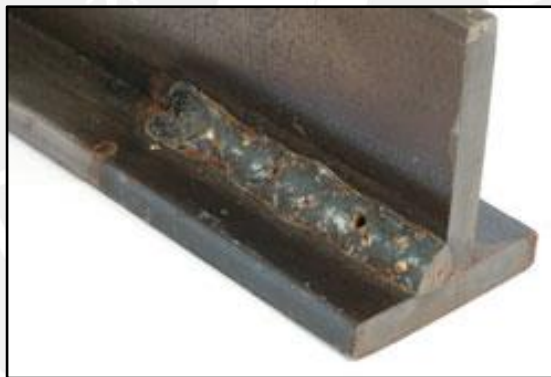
Porosidades en Cordón de Soldadura (<http://www.thefabricator.com>)
